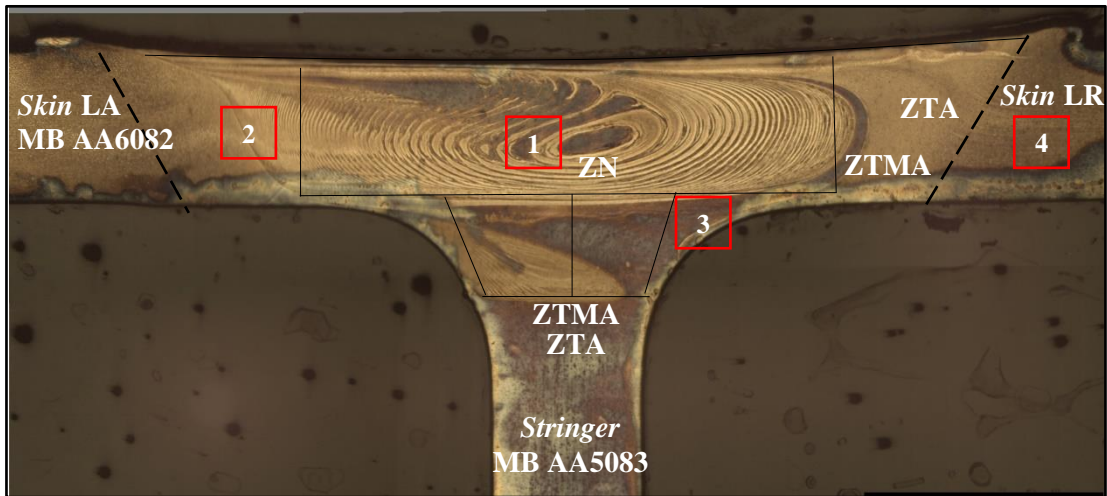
Distintas zonas formadas após a soldadura SFL no provete da série dissimilar 17\_65PP-60.
